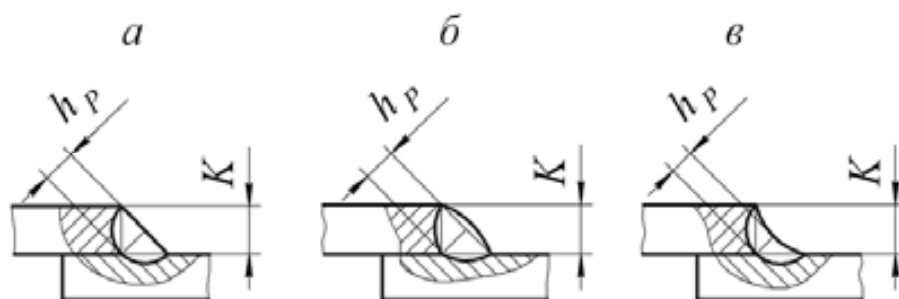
Форма угловых сварных швов: *а* – нормальный шов; *б* – выпуклый; *в* – вогнутый;  $hP$  – расчетная высота шва;  $K$  – катет шва
